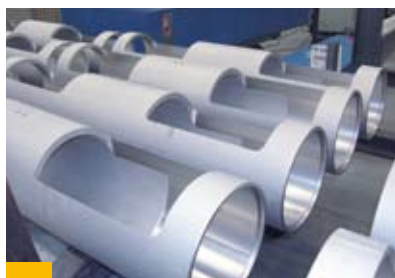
Grundrohr für eine Coriolis-Durchflussmesseinrichtung
